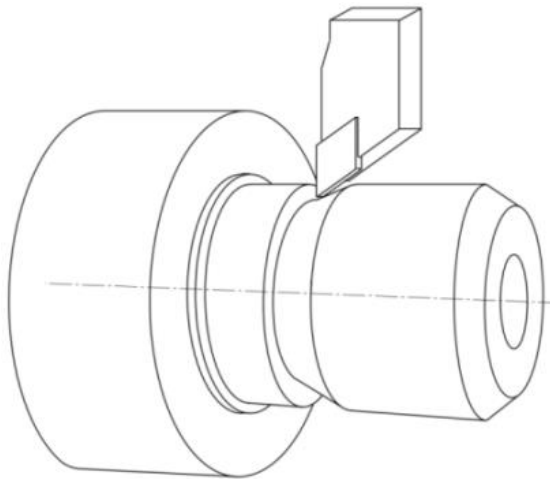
Süpürülmüş Kesici Takım Model Görüntüsü (Swept Cutting Tool Model View) [4]
